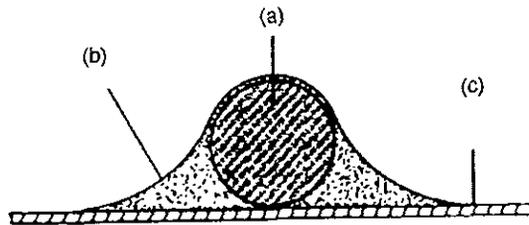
(a) Conductor, (b) Filete cóncavo, (c) La soldadura se va adelgazando hasta terminar en un canto delgado.
